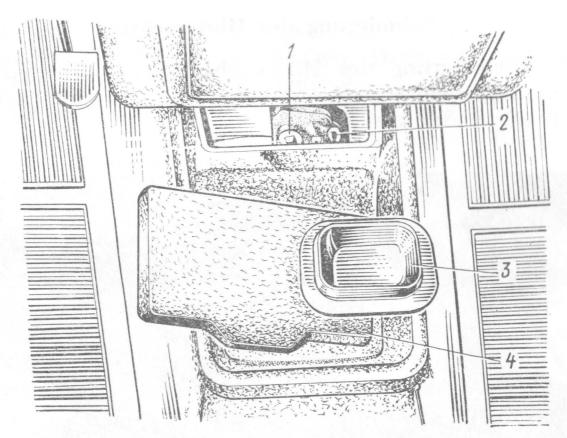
Lage von Einfüllöffnung und Ölmeßstab an Getriebekasten:
